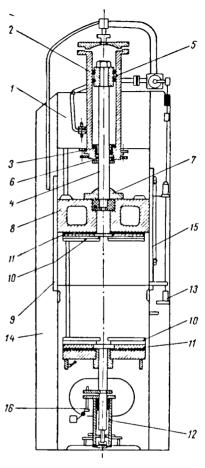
Рамный пресс верхнего давления ПВ-474:
